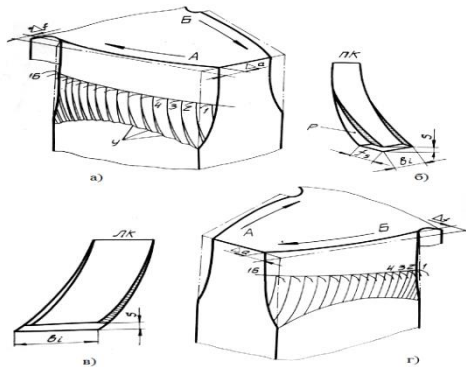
Форма слоев, срезаемых зубьями правозаходной фрезы с отдельной схемой формообразования: а - образование уступов (У) при работе правого корпуса; б - форма слоя, срезаемого зубьями правого корпуса; в - схема обработки поверхности зуба левым корпусом; г - форма слоя срезаемого зубьями левого корпуса
